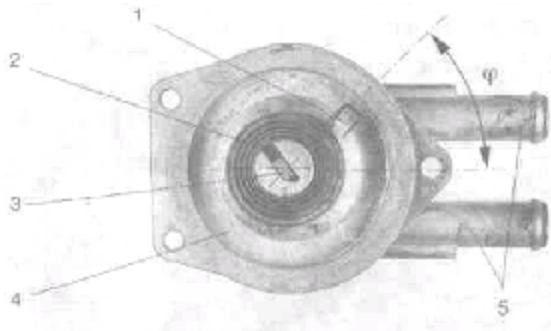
Нагревательный элемент пускового устройства с биметаллической пружиной:
